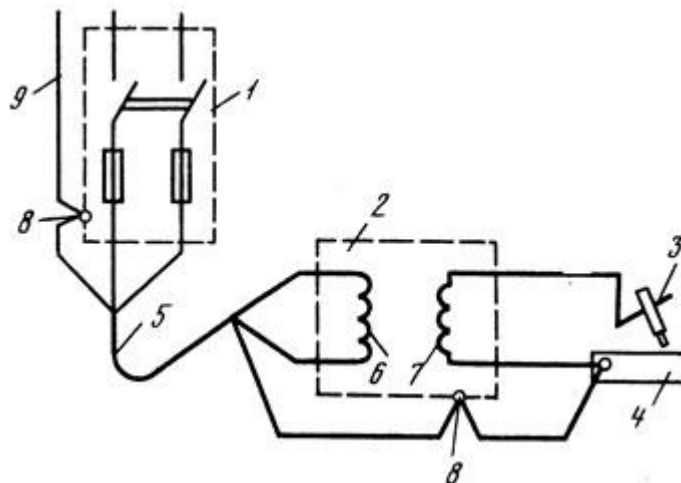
Схема подключения сварочного трансформатора при питании его от сети с глухозаземленной нейтралью: 1 – пункт подключения, 2 – сварочный трансформатор, 3 – электрододержатель, 4 – свариваемое изделие, 5 – питающий шланговый трехжильный провод с заземляющей жилой, 6 – первичная обмотка трансформатора, 7 – вторичная обмотка трансформатора, 8 – заземляющий болт на корпусе трансформатора и на пункте подключения, 9 – к нулевому проводу сети
